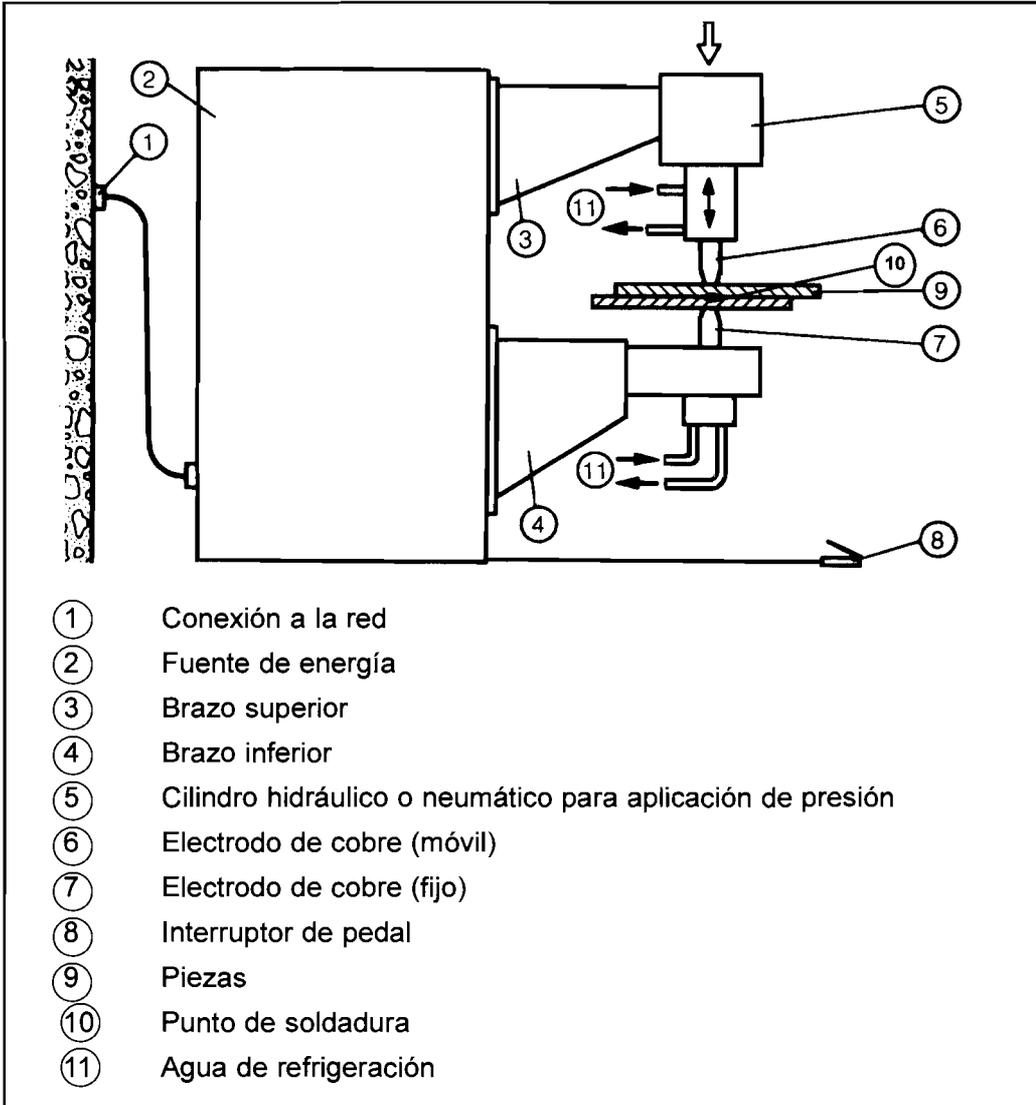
EQUIPO DE SOLDEO POR PUNTOS
